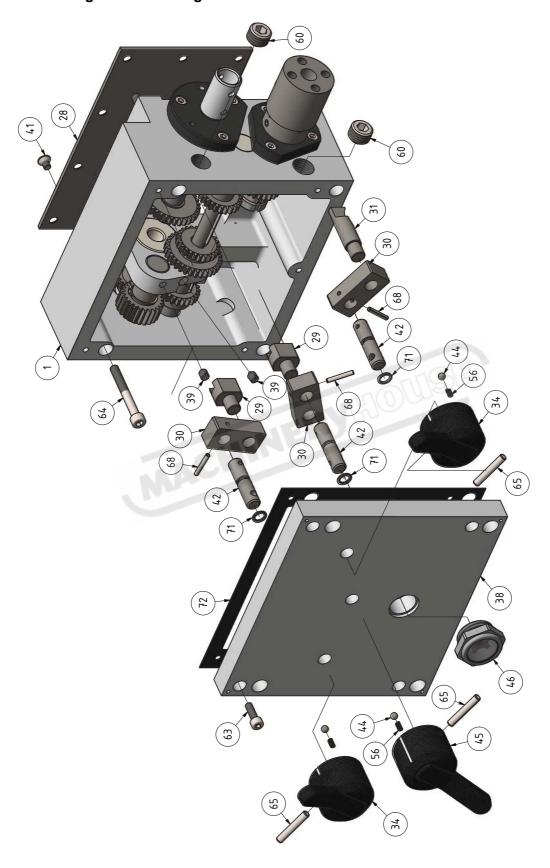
Vorschubgetriebe - Feed gear 1-2
